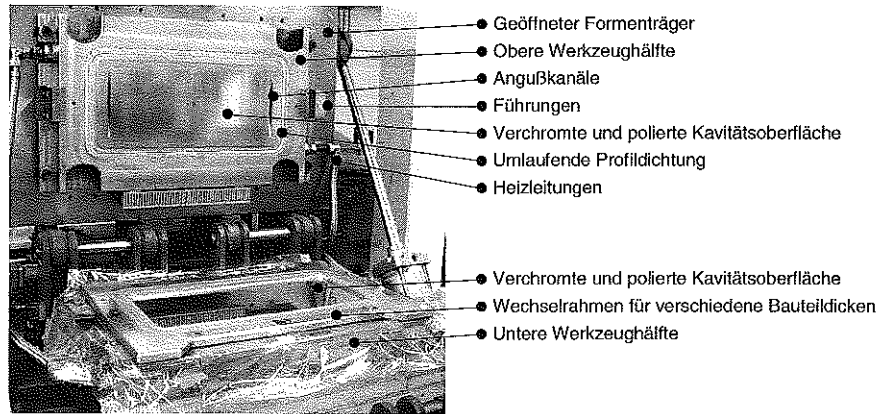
RTM-Werkzeug im Einsatz auf dem Formenträger
